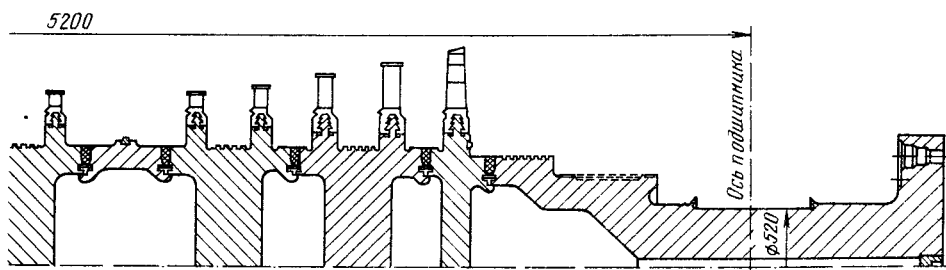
Сварной ротор ЦВД турбины К-500-65/3000 ХТЗ
